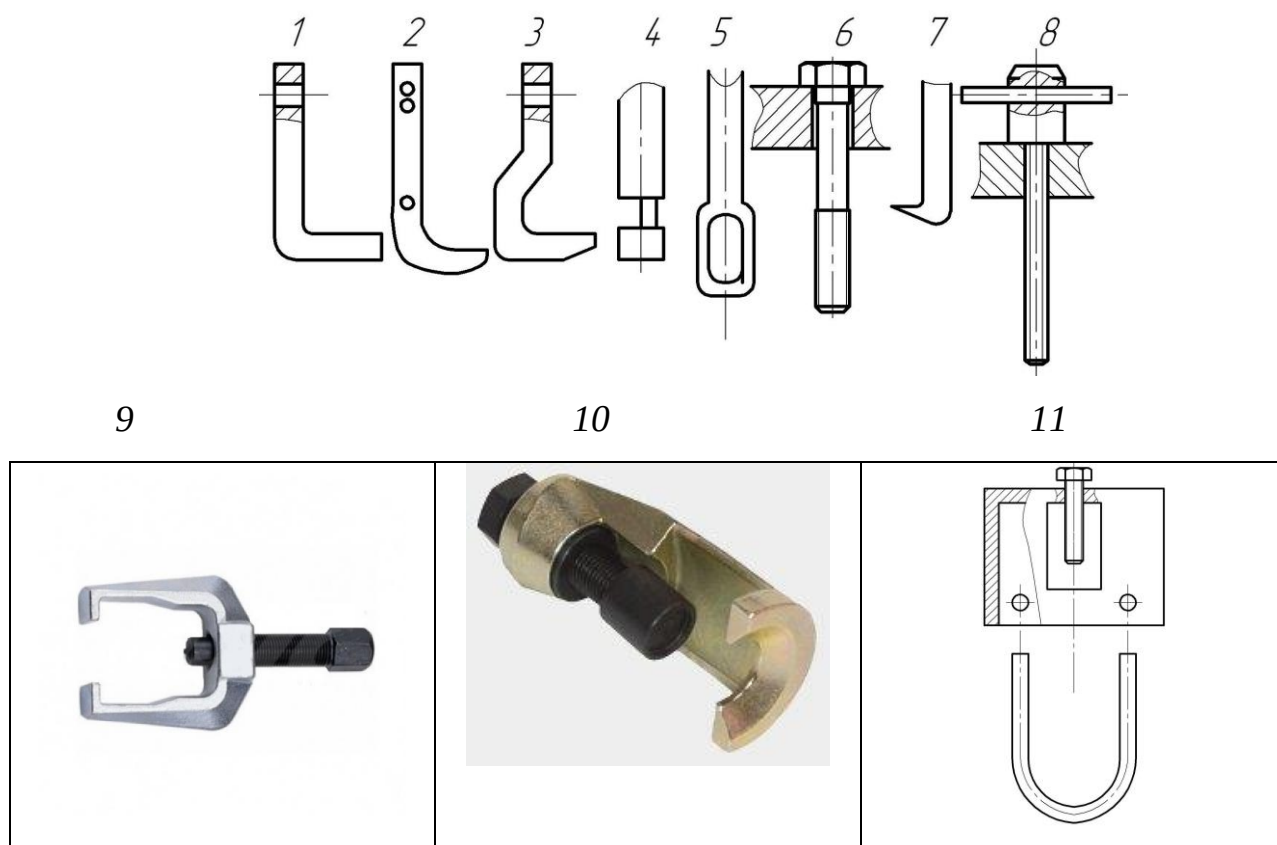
Захваты различной формы: 1, 2, 3 и 7 – лапчатые простые; 4 – эксцентриковый; 5, 6 и 8 – захваты-тяги; 9 и 10 – захваты, жестко связанные с корпусом; 11 – захват-вилка
